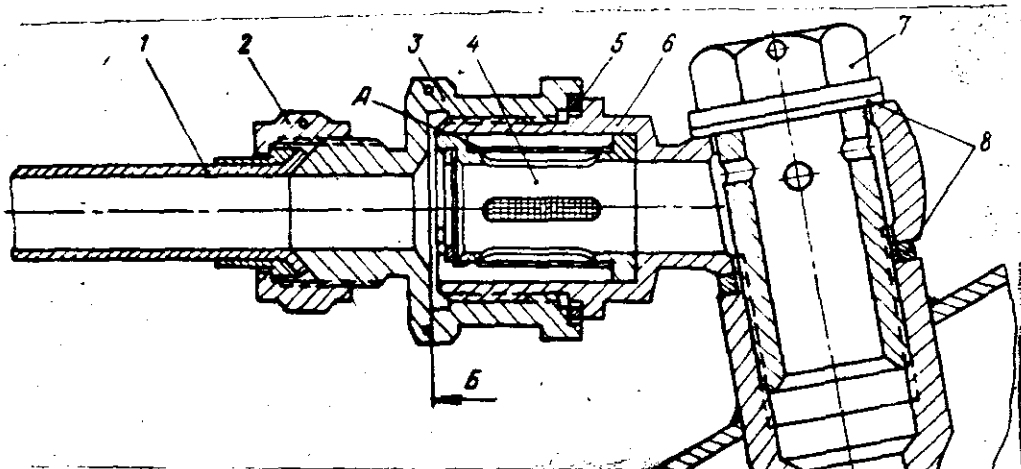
Замена фильтра в трубопроводе подвода масла на смазку заднего подшипника компрессора и подшипника турбины:
